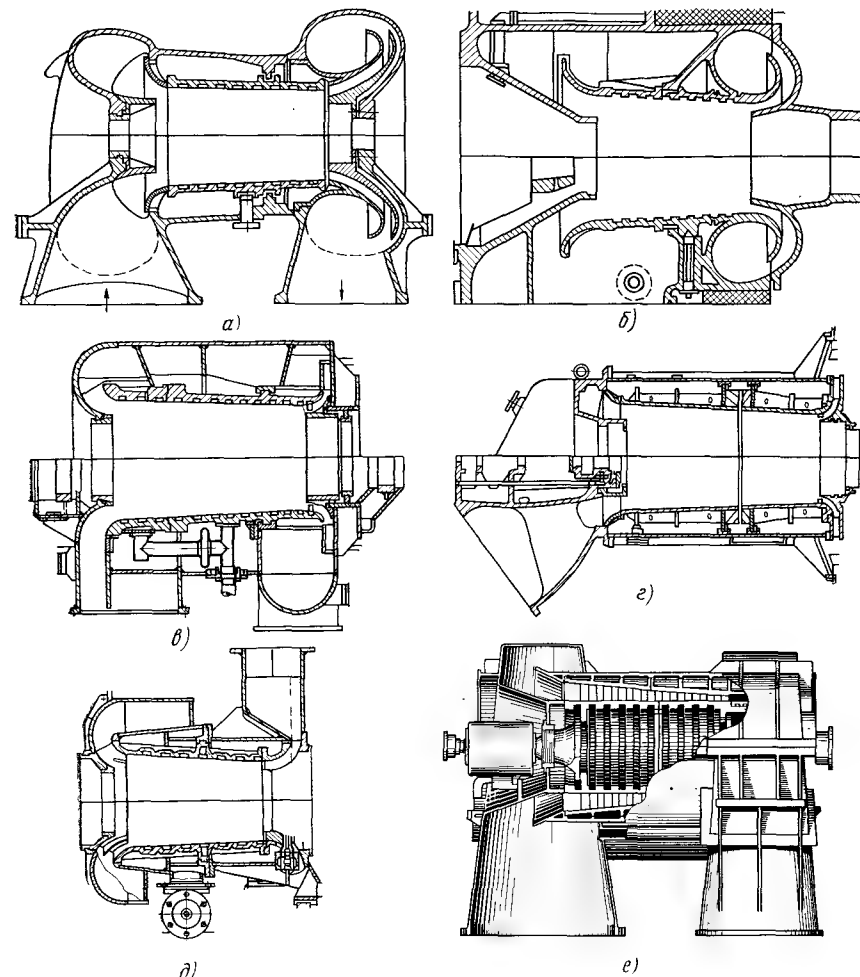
Двухстенные корпуса компрессоров ГТУ:
